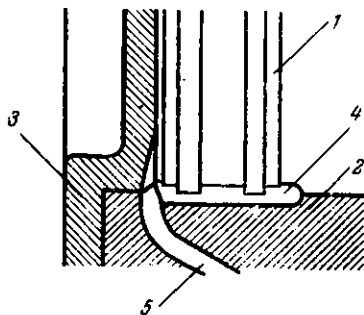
Канавка в зеркале цилиндра для выравнивания давлений: 1 — поршень; 2 — цилиндр; 3 — крышка цилиндра; 4 — канал перепускной; 5 — канал к золотнику.
